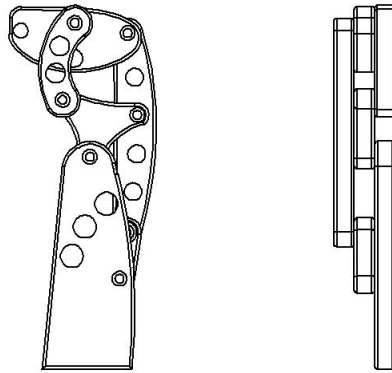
(A) vista lateral y (b) frontal del mecanismo de barras. Solidworks©
